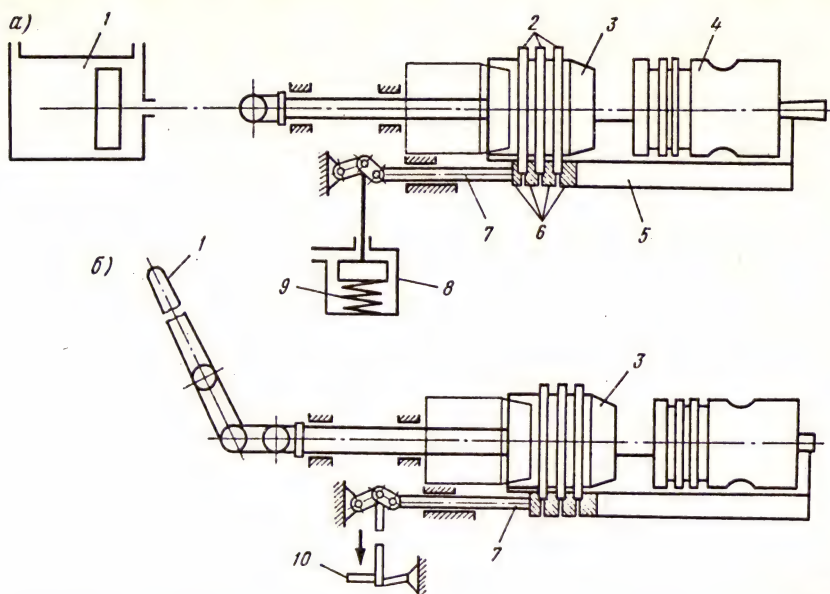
Приспособления для одновременной установки поршневых колец на поршень:
